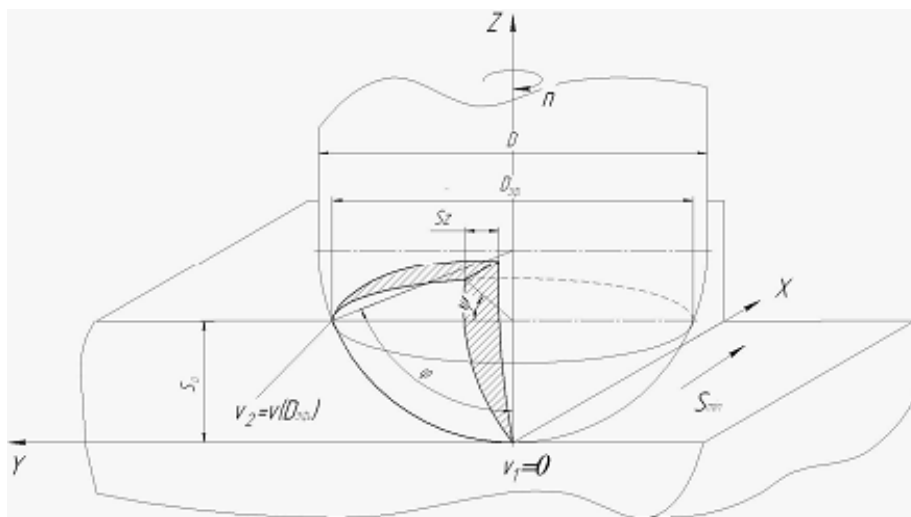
Змінний переріз зрізу при обробці сферичною кінцевою фрезою
